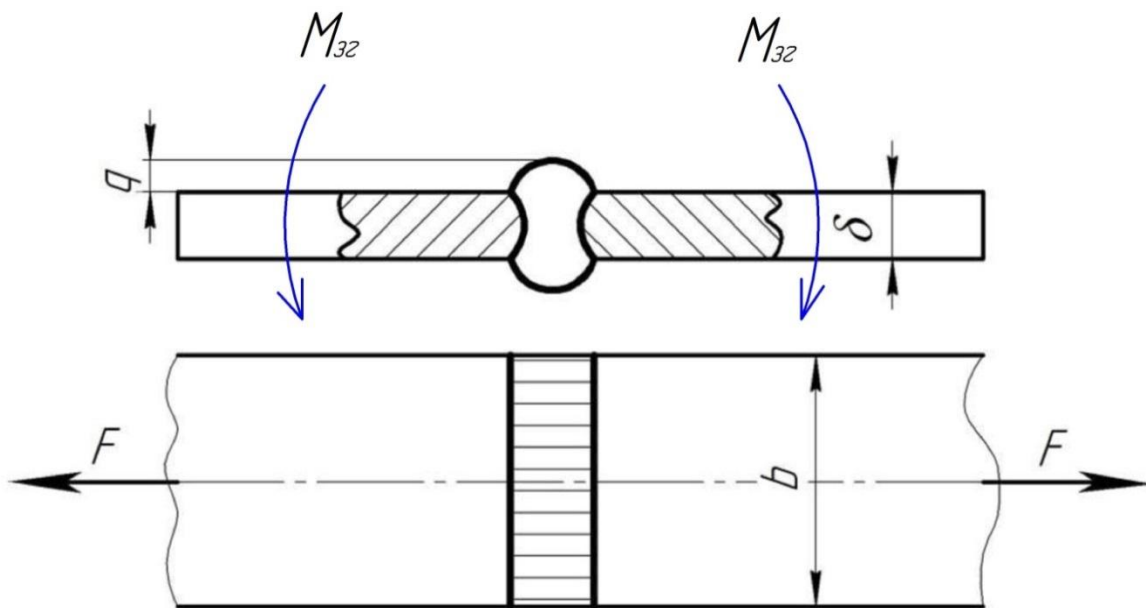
Розрахункова схема зварного з'єднання стиковим швом
